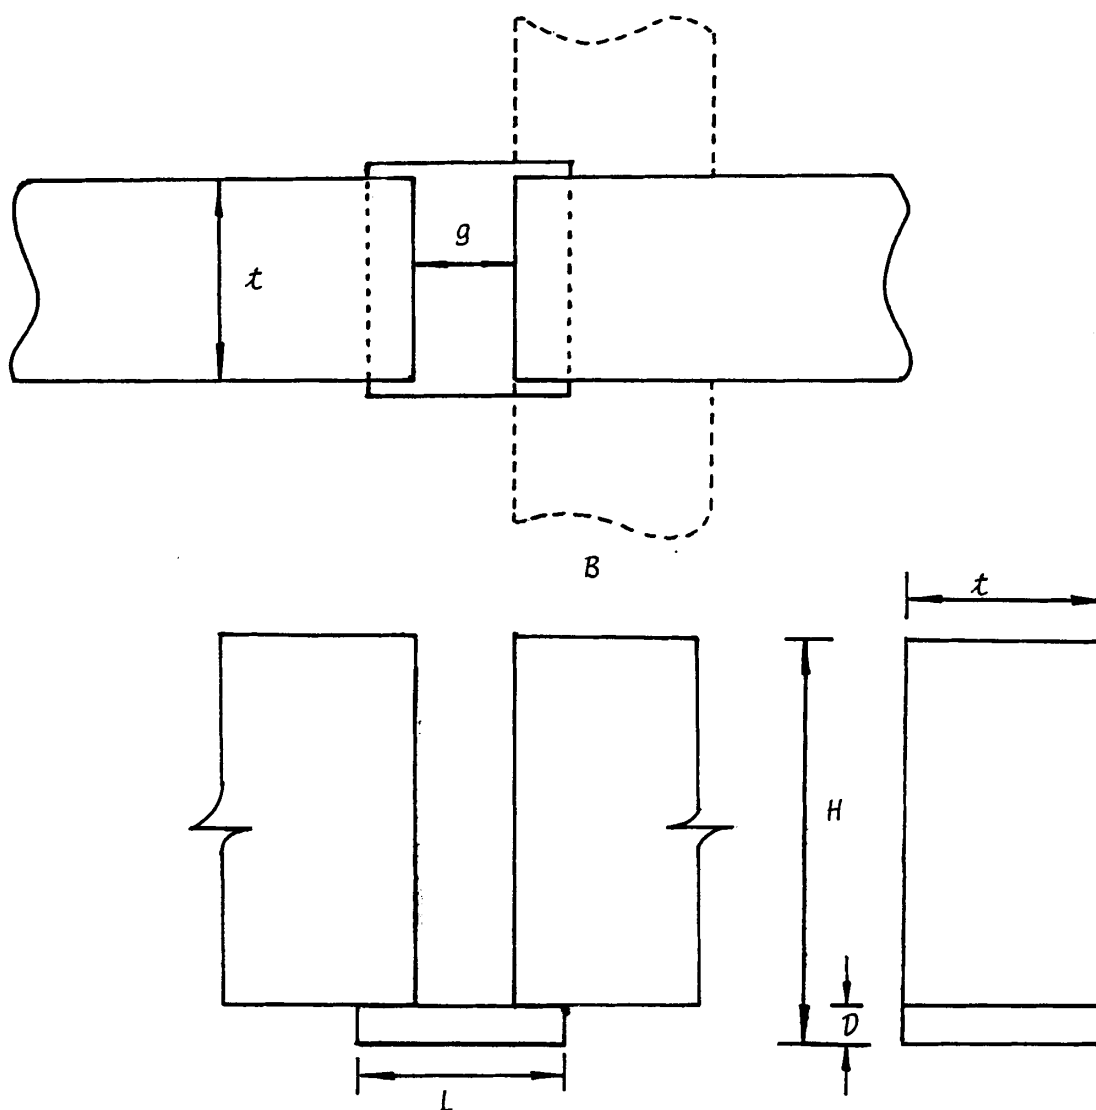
ESQUEMA DE LA GEOMETRIA RECTANGULAR A SOLDAR MOSTRANDO LAS DIMENSIONES.
